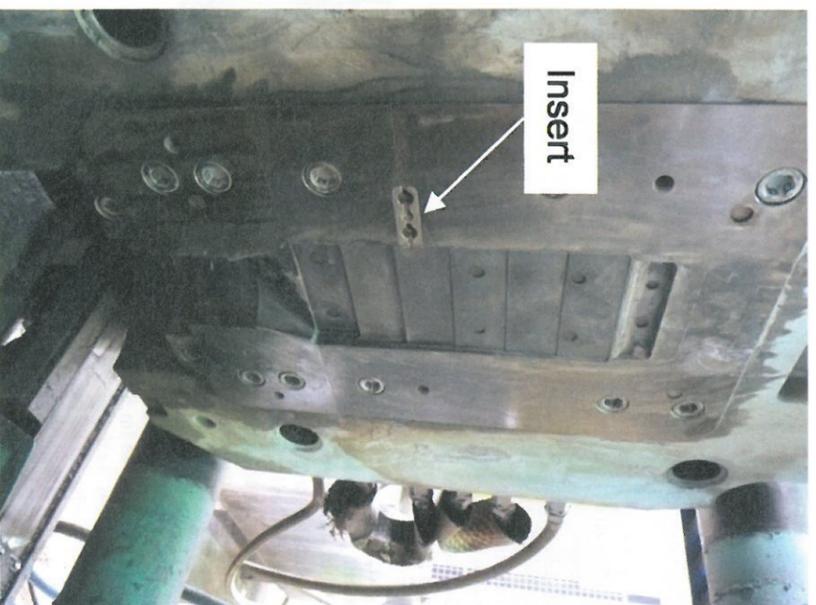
Kokille mit Insert, Squeeze Casting Verfahren am LKR
